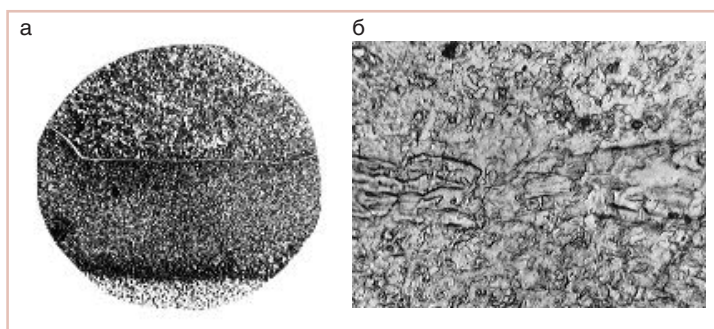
Приварка медного проволочного вывода диаметром 1 мм к колпачку из томпака толщиной 0,35 мм с никелевым покрытием,  $\delta = 12$  мкм: а — стыковая сварка сопротивлением,  $\times 100$ ; б — УКС,  $\times 600$
